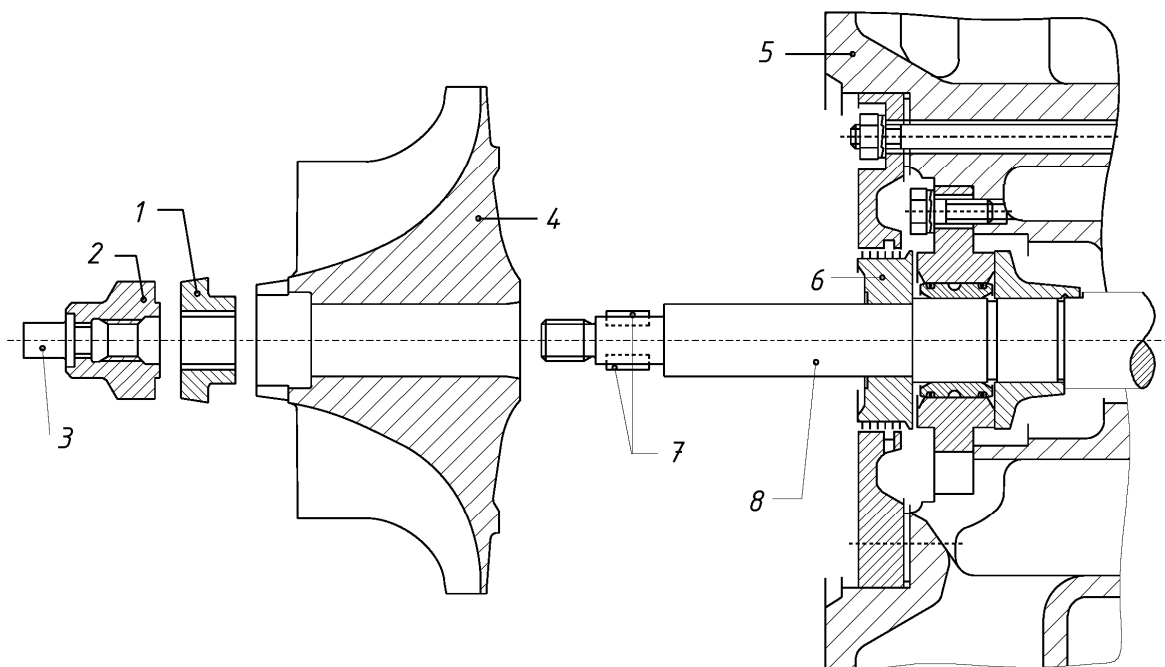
Демонтаж і монтаж колеса компресора. 1 – опорна втулка; 2 – гайка; 3 – стопор; 4 – колесо компресора; 5 – корпус ТК; 6 – ущільнення; 7 – шпонка; 8 – вал
